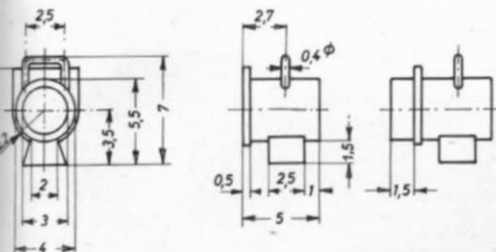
Bauzeichnung für Laternen zur Ausleuchtung mit handelsüblichen, gesockelten Kleinstbirnen. Die linke Seitenansicht zeigt die Ausführungsform der vorderen Laternen, die rechte die der rückwärtigen. Zeichnung im Maßstab 2:1.
